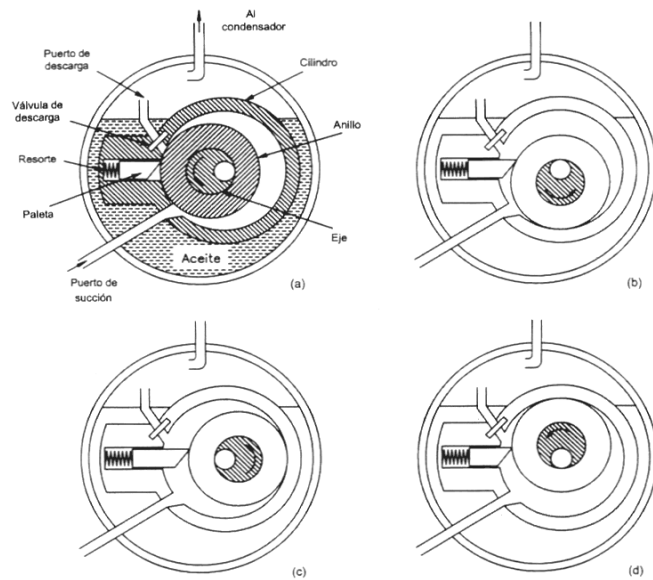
Compresor rotativo de tipo de excéntrica
